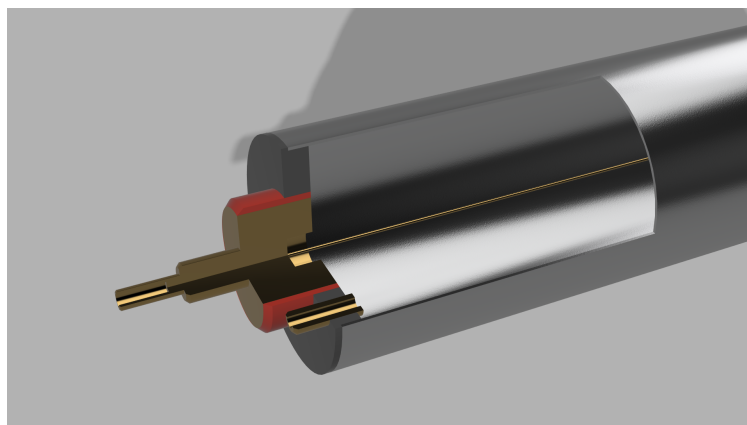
Вид straw детектора из металлической трубы в разрезе
